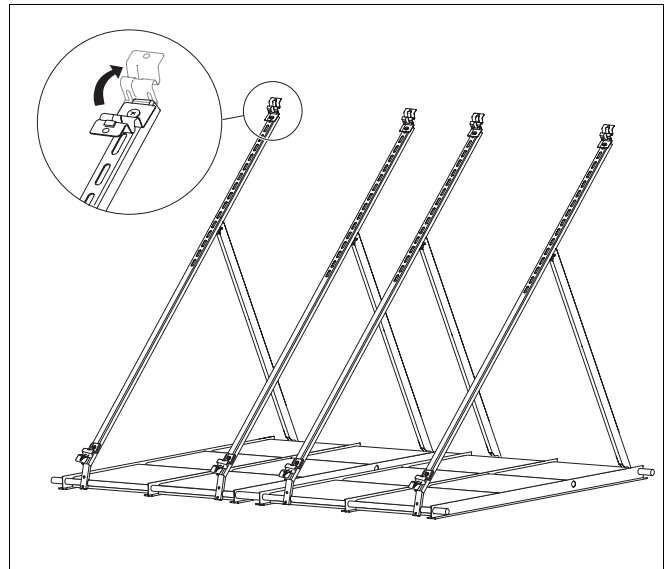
Gesamtansicht Flachdachständer – senkrechte Ausführung für zwei Kollektoren
